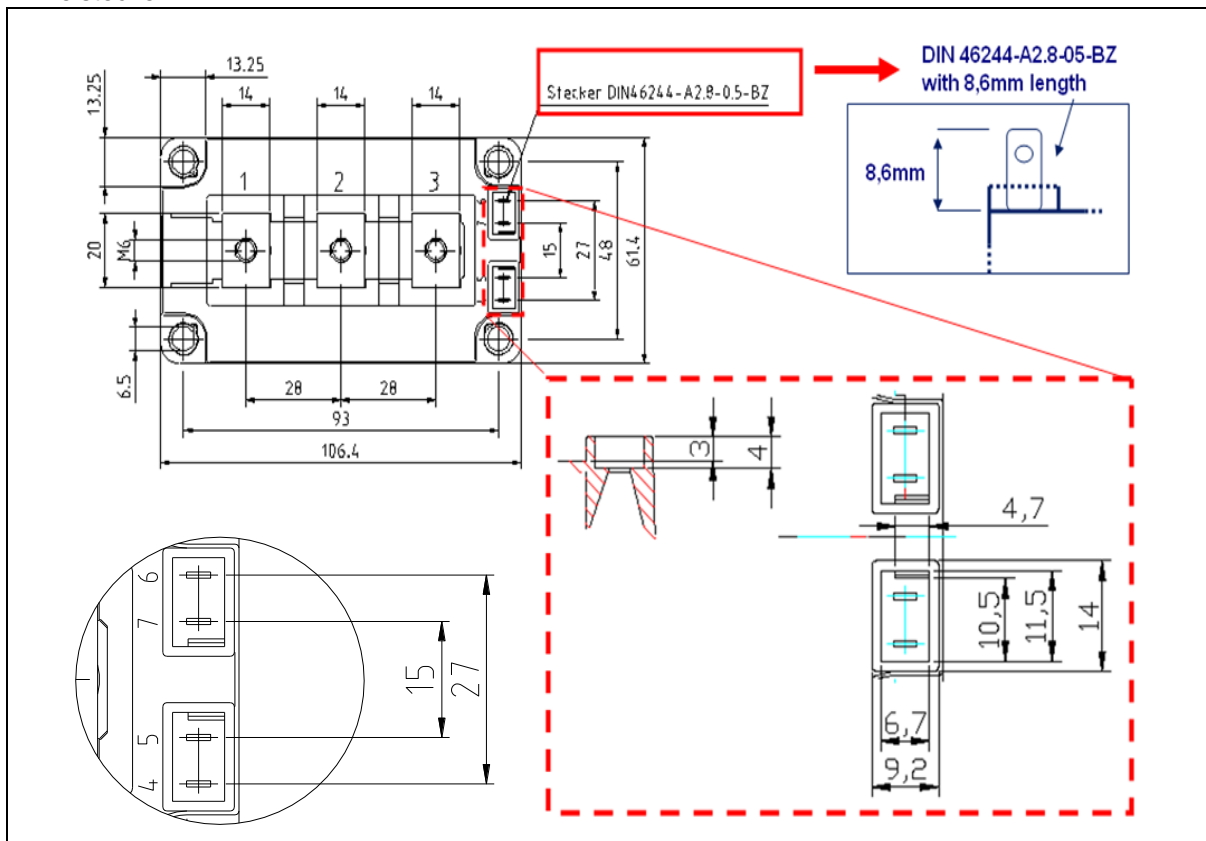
Detailzeichnung des Steuerkontaktgehäuses in der 62mm Halbbrücken Gehäusevarianten
